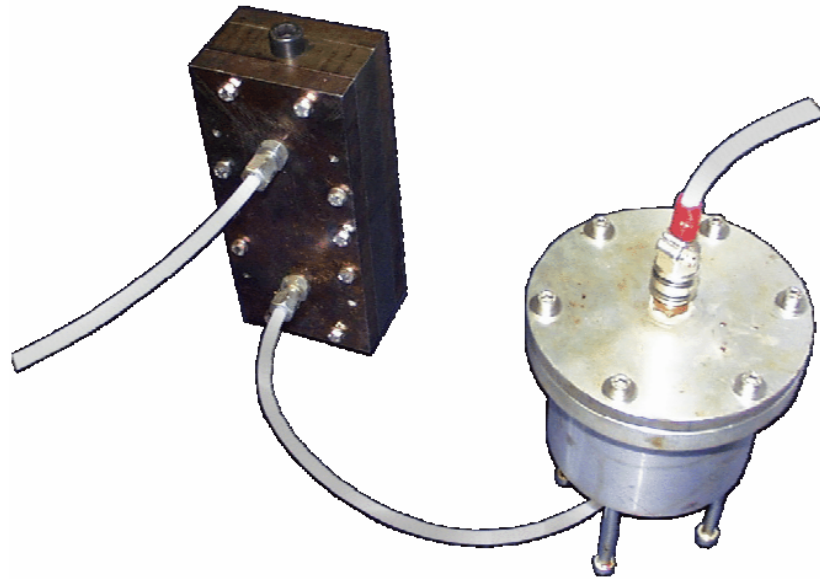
RTM-Werkzeug für die endkonturnahe Infiltration von Celanese-Druckproben
